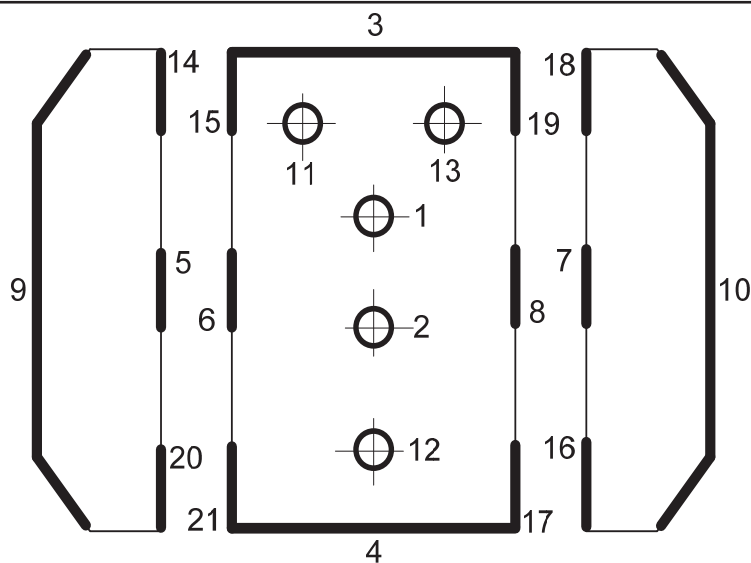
Последовательность наложения сварных швов при приварке наличников
